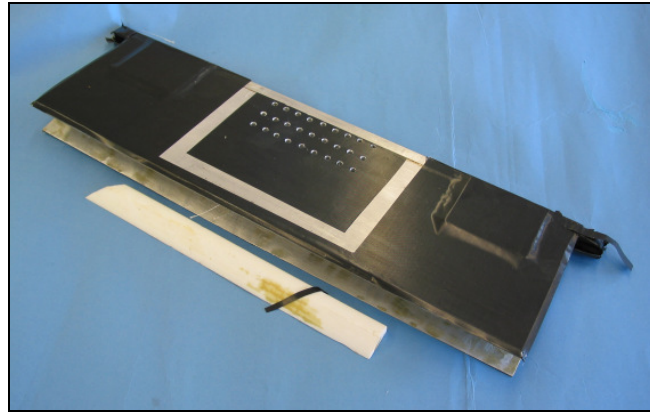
Fertigungswerkzeug für Schlaufen in Textiltechnik
